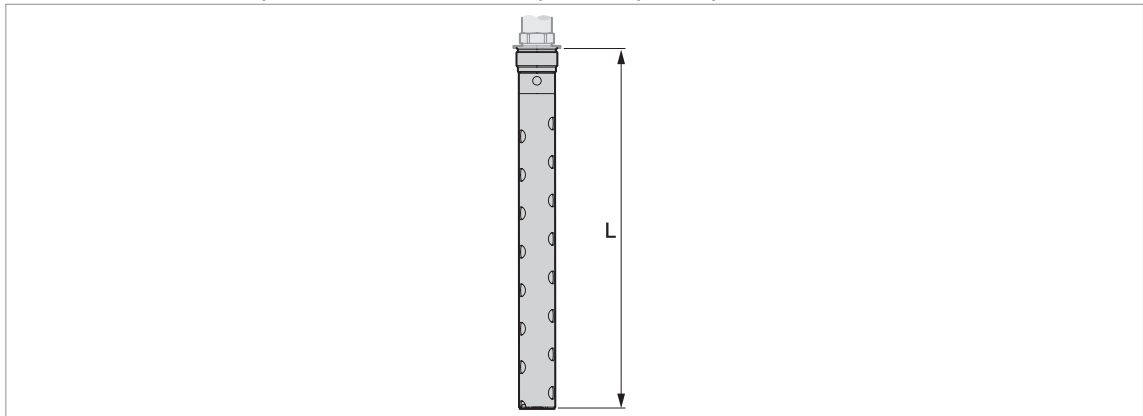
Коаксиальный сенсор: опции и общие габаритные размеры
